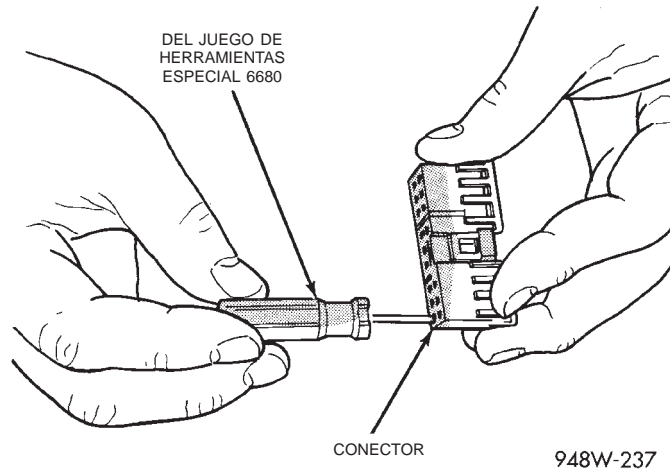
Desmontaje de terminal utilizando la herramienta especial
